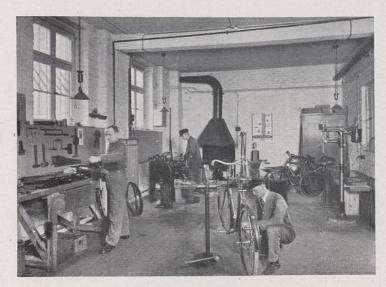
Duisburg. Ausbesserei für Fahrräder und Wirtschaftsgegenstände.
